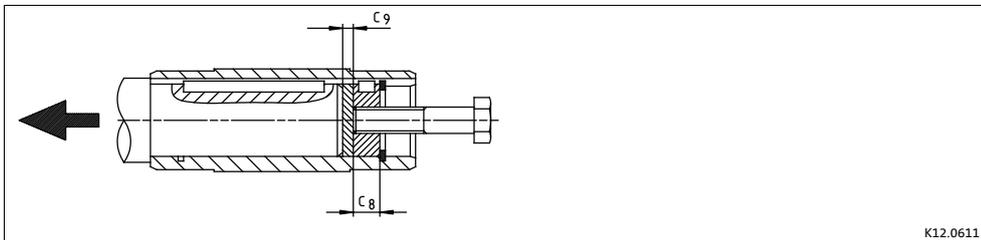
Demontage von Getrieben mit Hohlwelle, mit Hilfswerkzeug; nicht für GKR
